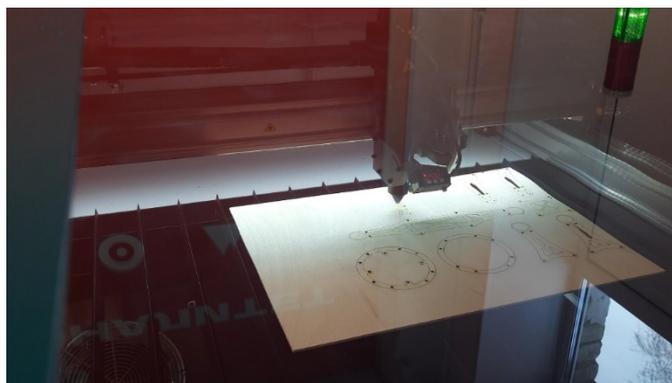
Процесс лазерной резки деталей на станке с ЧПУ Cutter ML
